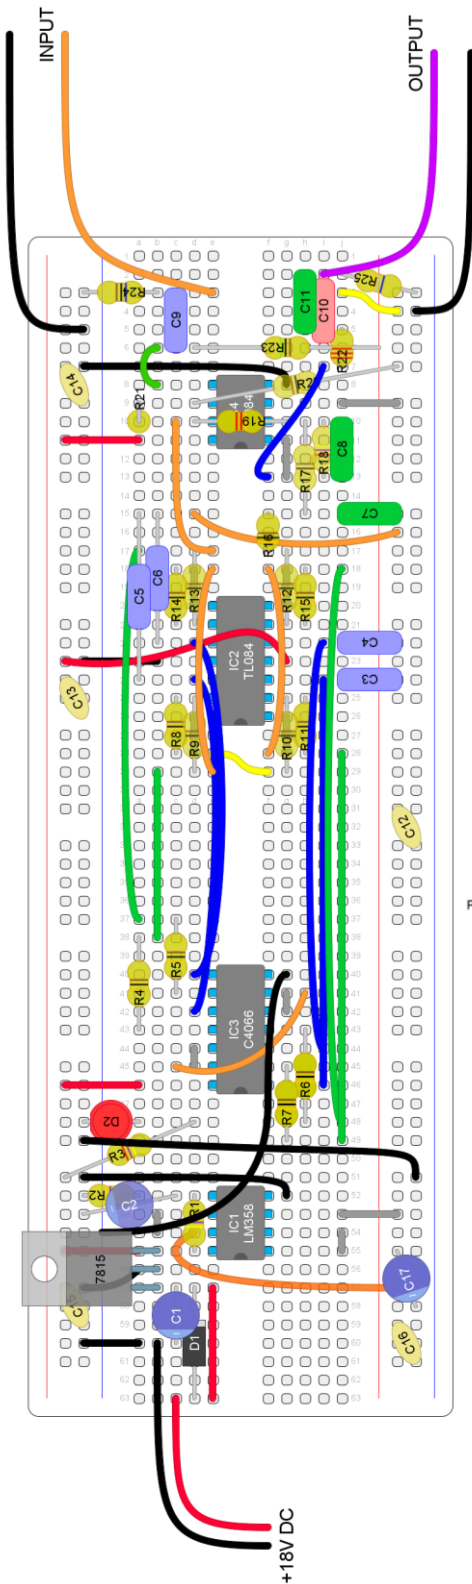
Layout sezione di alimentazione e parte analogica dell'effetto audio.
